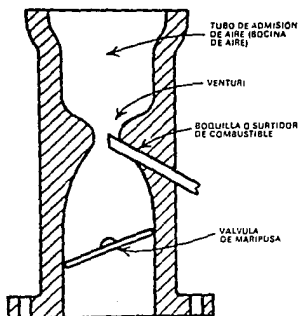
Carburador elemental compuesto de un tubo o canal de paso de aire, un surtidor o boquilla de combustible y una válvula de mariposa.
